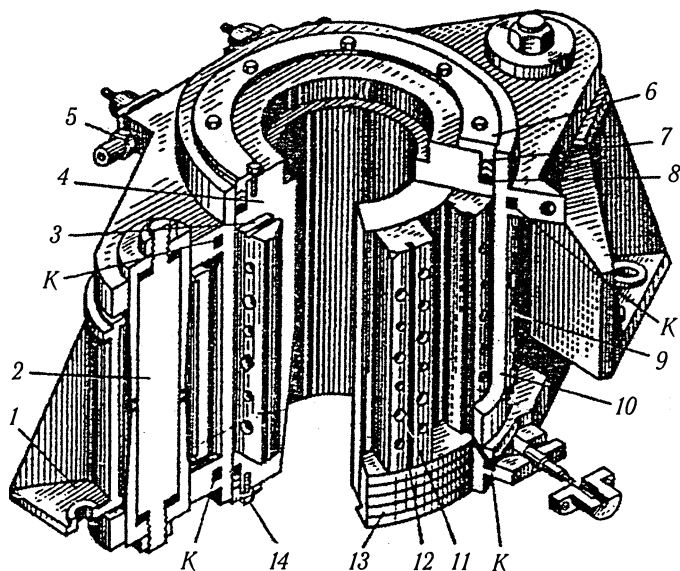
Рулевой лопастный привод фирмы AEG Schiffbau: 1 — подшипник, 2 — ось, 3 — неподвижная лопасть, 4 — ротор, 5 — запорный вентиль, 6 — нажимное кольцо, 7 — кольца сальника, 8 — резиновое кольцо, 9 — болт крепления неподвижной лопасти, 10 — цилиндр, 11 — подвижная лопасть, 12 — уплотнительная пластина. 13 — кольца сальника, 14 — болт, К — каналы рабочей жидкости
